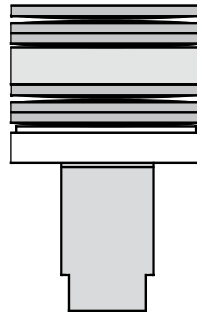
Montaje correcto del adaptador de válvula al actuador EL565
